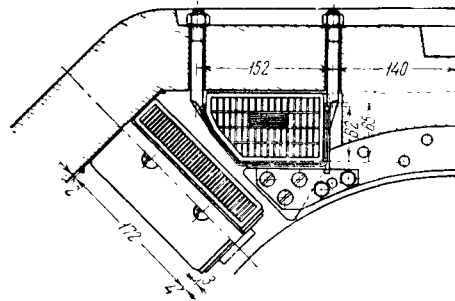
Щёткодержатели двигателя типа НБ-406А и их установка:
